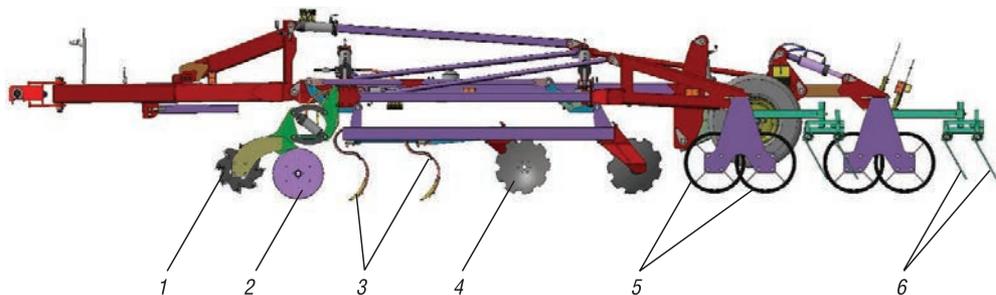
Конструктивная схема агрегата почвообрабатывающего АПМ-6 (вид сбоку)
